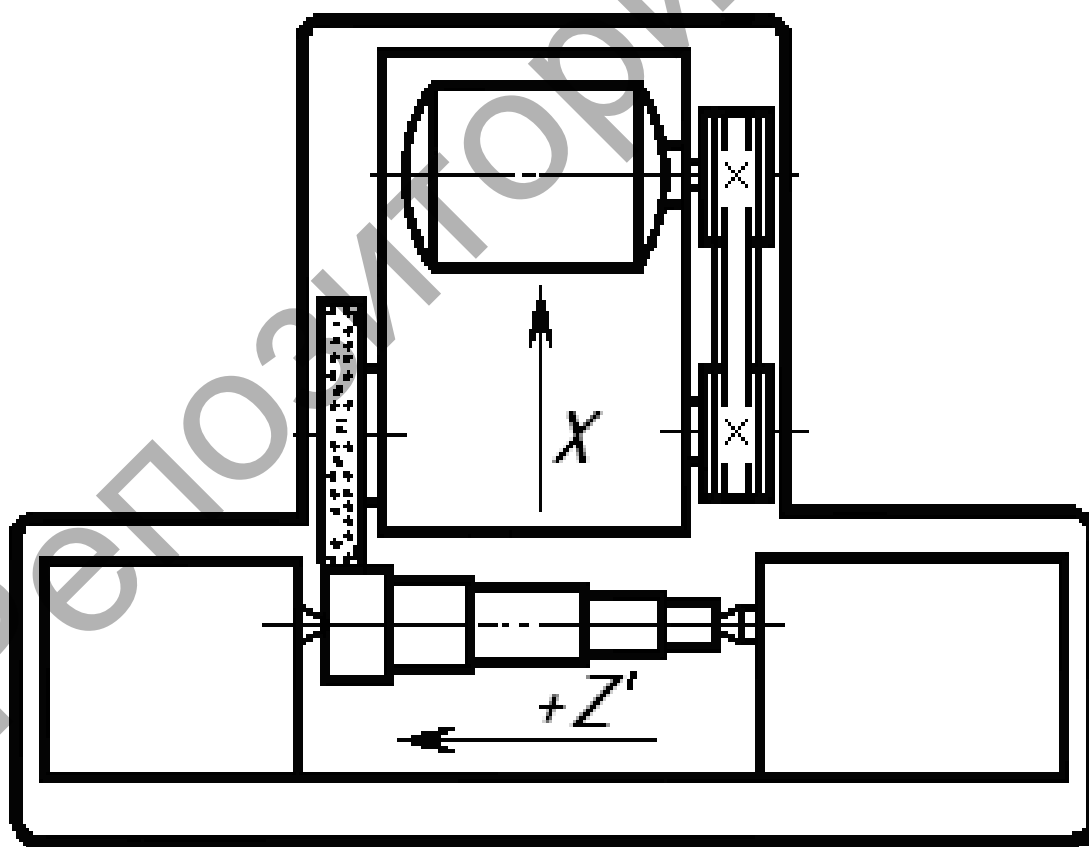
Система координат круглошлифовального станка с ЧПУ
